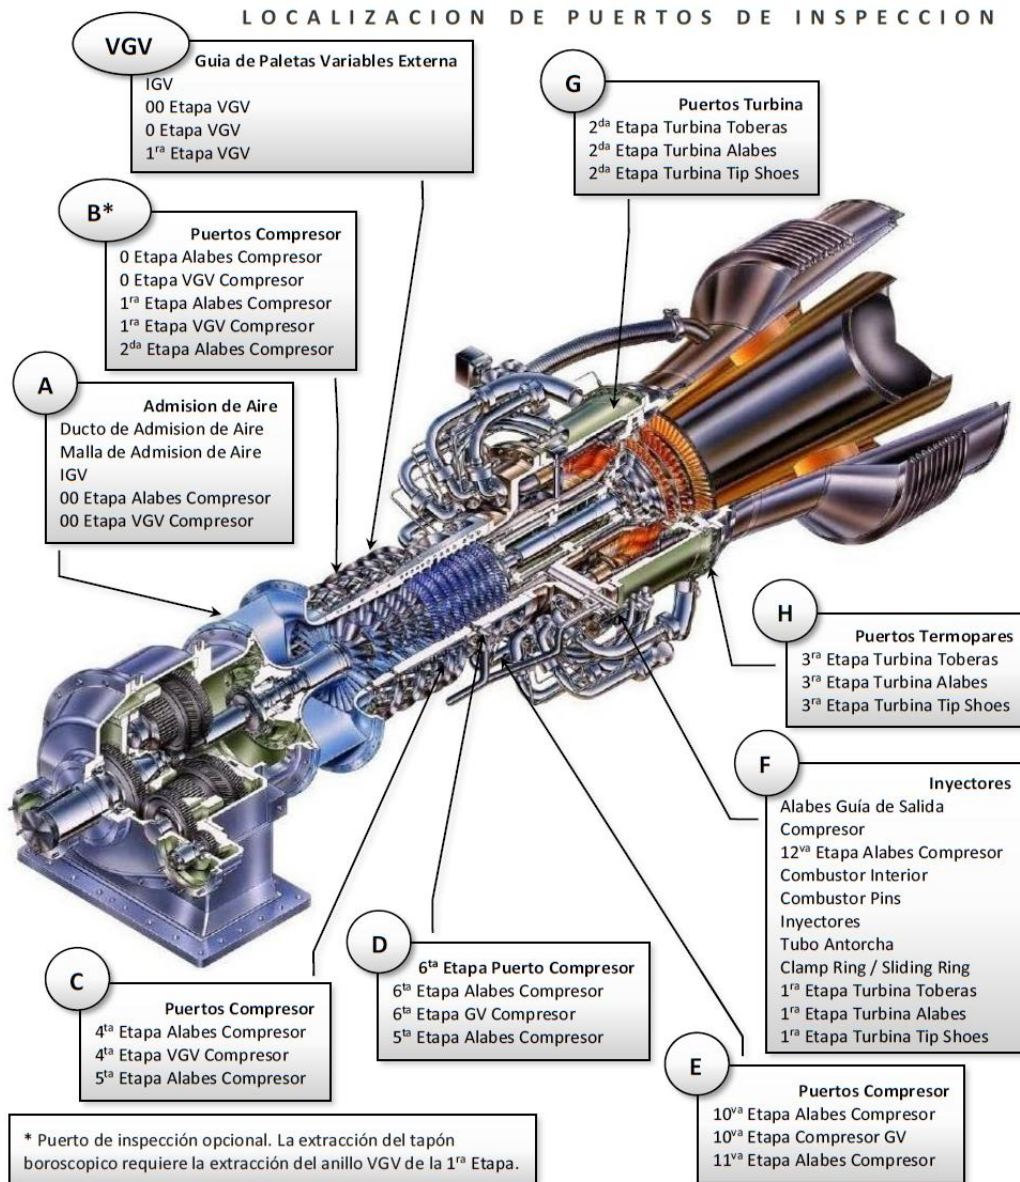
Partes de turbina Taurus 70. Fuente: <https://lc.cx/rsRmRc>
